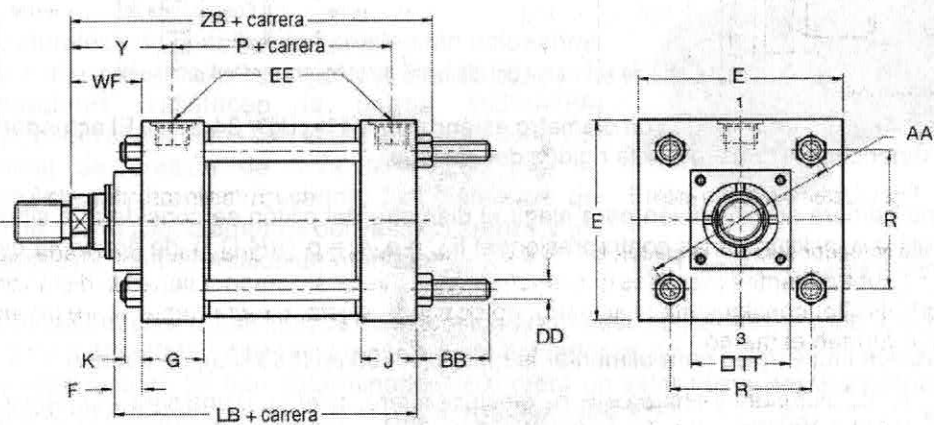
Dimensiones del actuador con montaje MX2 de la NFPA.
